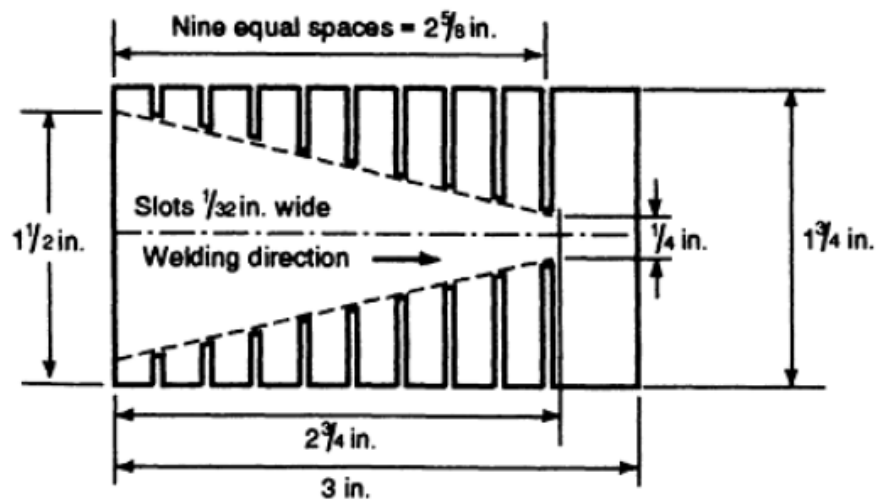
Dimensiones del espécimen para el ensayo Houldcroft⁹⁷
